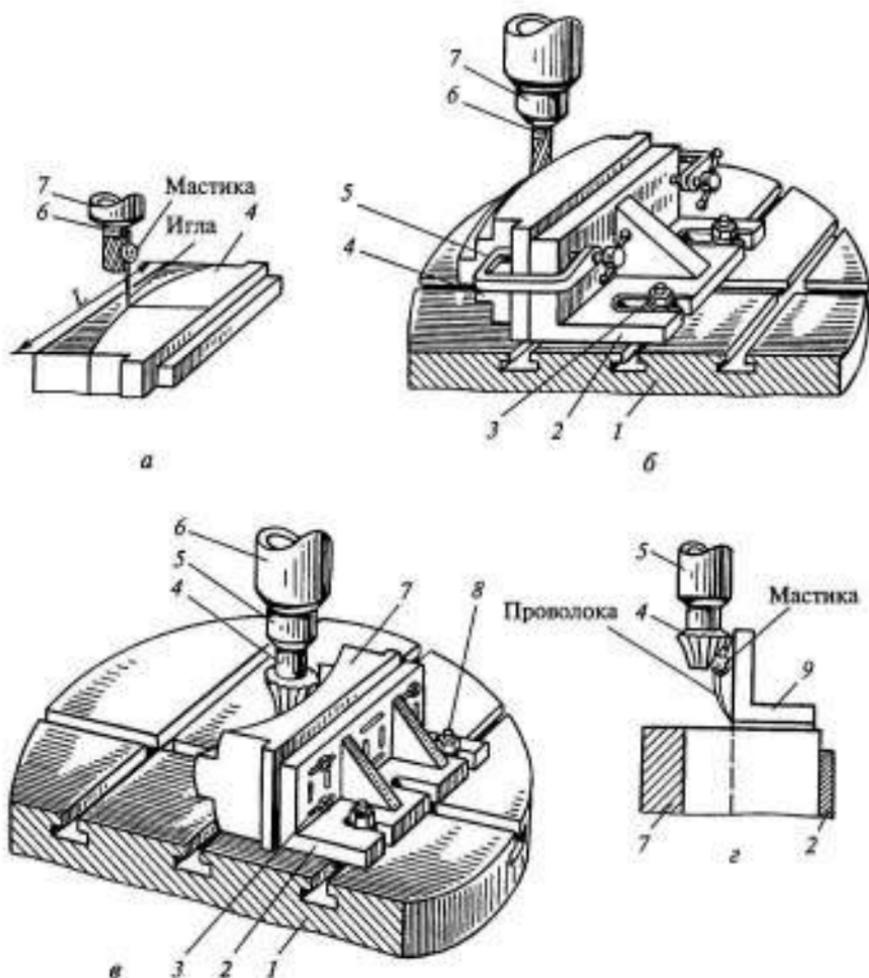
Приемы фрезерования больших заготовок для получения выпуклых и вогнутых поверхностей:
